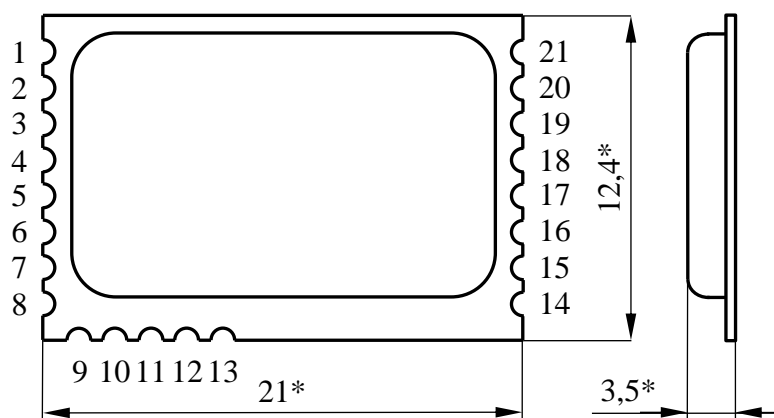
Габаритный чертёж ЕВТС101 (размеры в мм)
